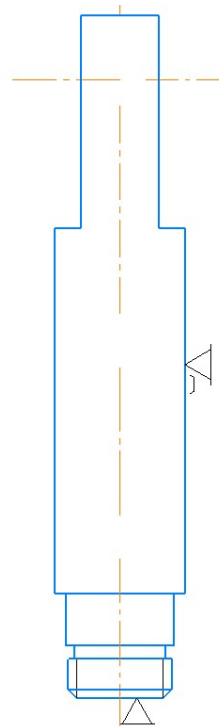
Схема базування заготовки при обробці поверхонь лиски
